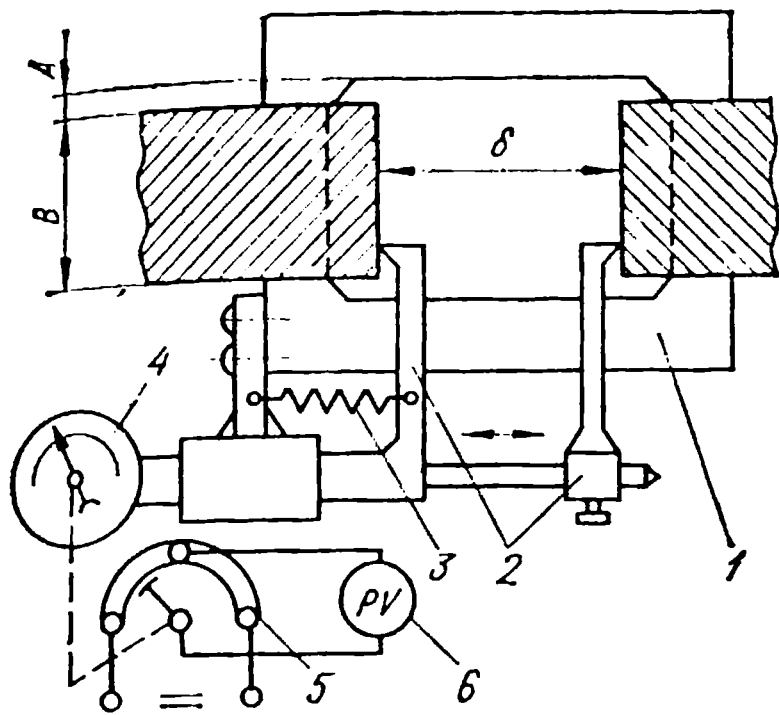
Потенциометрический датчик сварочного зазора:
